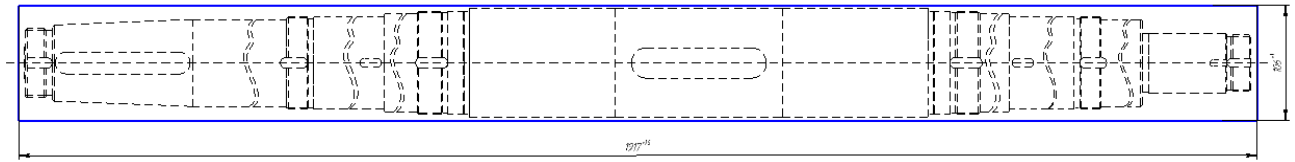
Вигляд заготовки, що отримується ковкою на молотах
